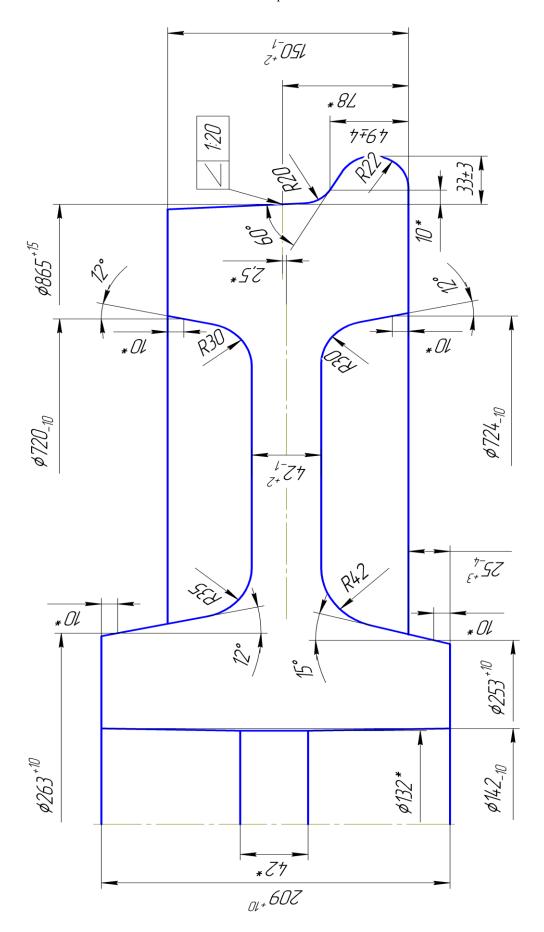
Колесо без механической обработки (после проката) \varnothing 865 мм, под чистовое \varnothing 850 мм, чертеж №КР-0047-11. Масса колеса - 472 кг.
